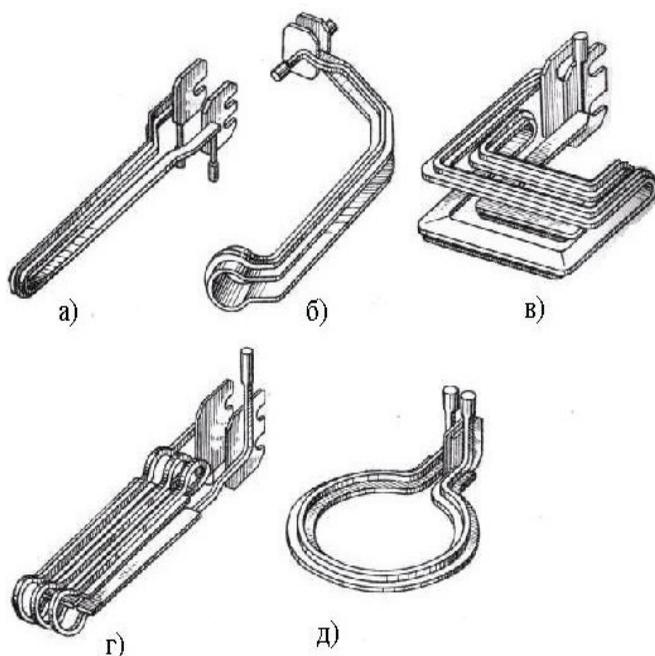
Индукторы для наплавки различных деталей машин:
